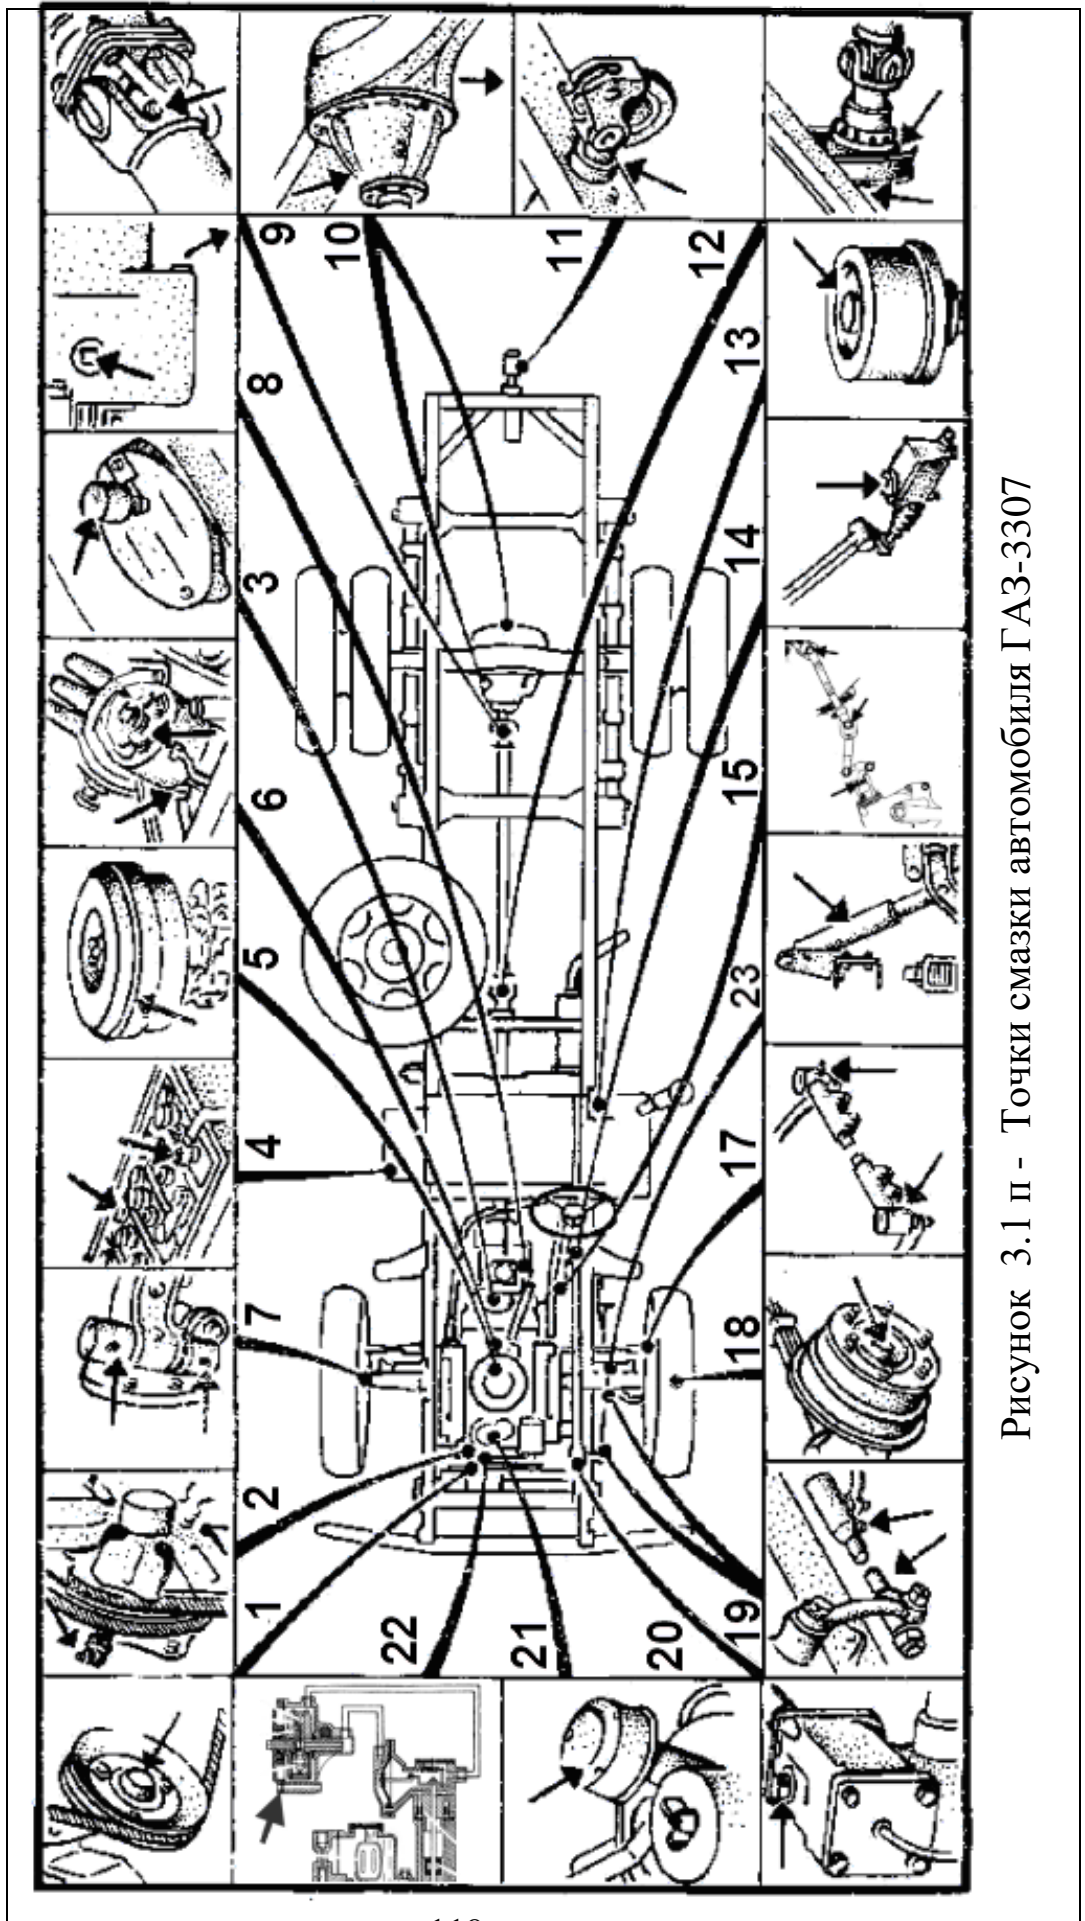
п - Точки смазки автомобиля ГАЗ-3307
